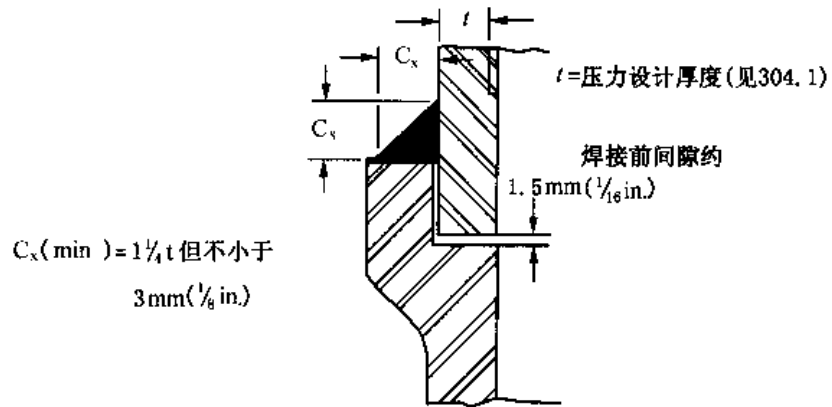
C 除法兰外的承插焊组件的最小焊接尺寸
